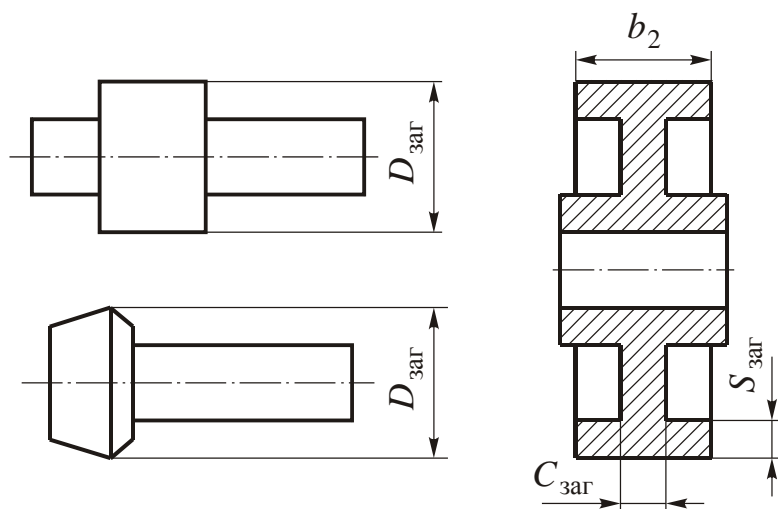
Размеры заготовок (слева – шестерен, справа – колес)
